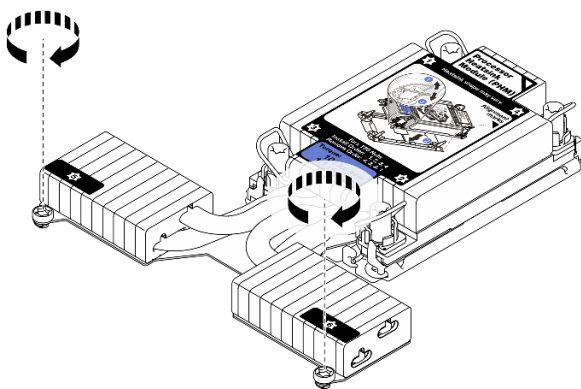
Serrage des vis du dissipateur thermique en forme de T
